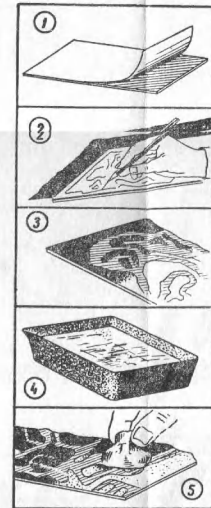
Изготовление самодельного фольгированного гетинакса:
